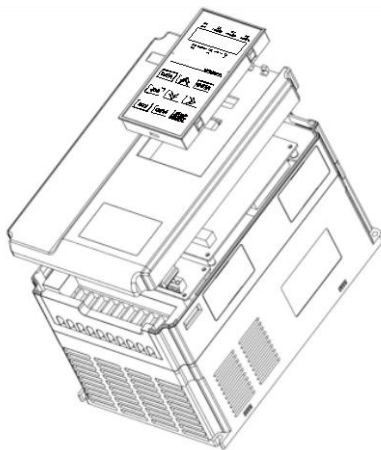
Схема демонтажа нижней крышки пластикового корпуса
